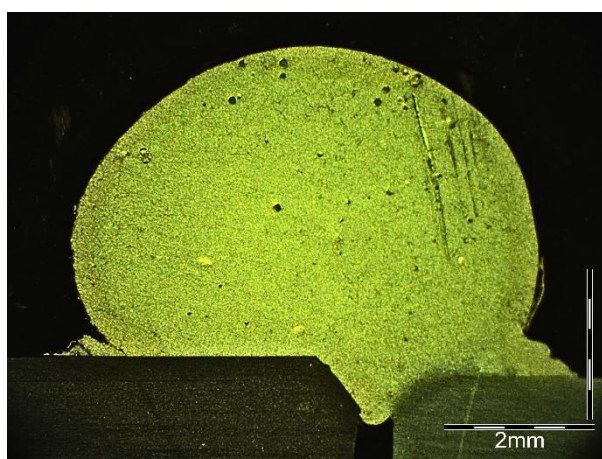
Macrografia do cordão de solda dissimilar Ti-Al, condição 6, energia 2,41 kJ/cm.
